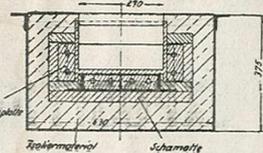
Coupe perpendiculaire à la direction du fil du four à galvaniser. Type III; puissance 6 kW.
